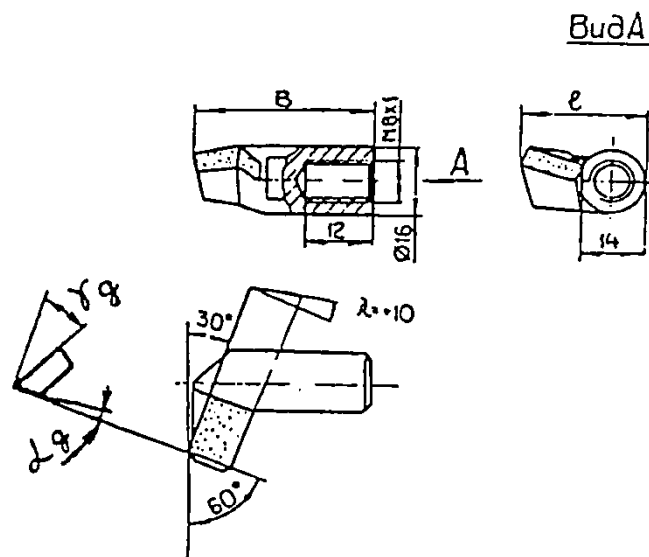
Резцы обработки внутренних поверхностей
